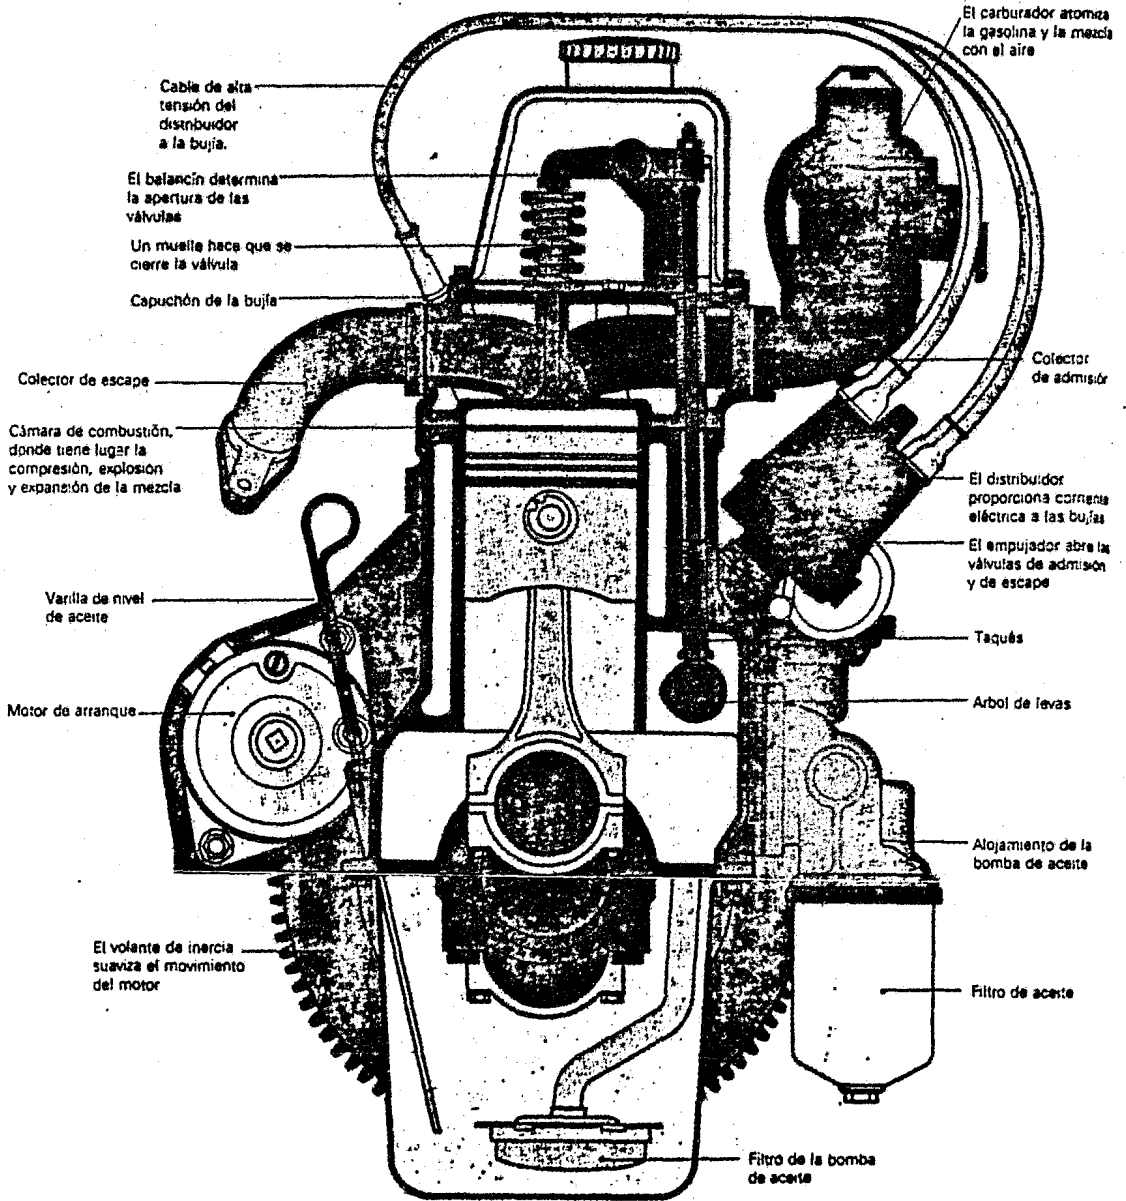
SECCION LATERAL DE UN MOTOR DE EXPLOSIÓN DE 4 CILINDROS
